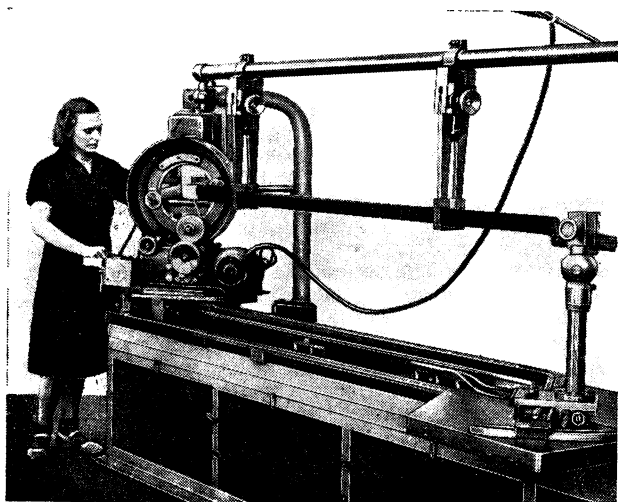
Фото изолировочного станка ЛШ-5.
